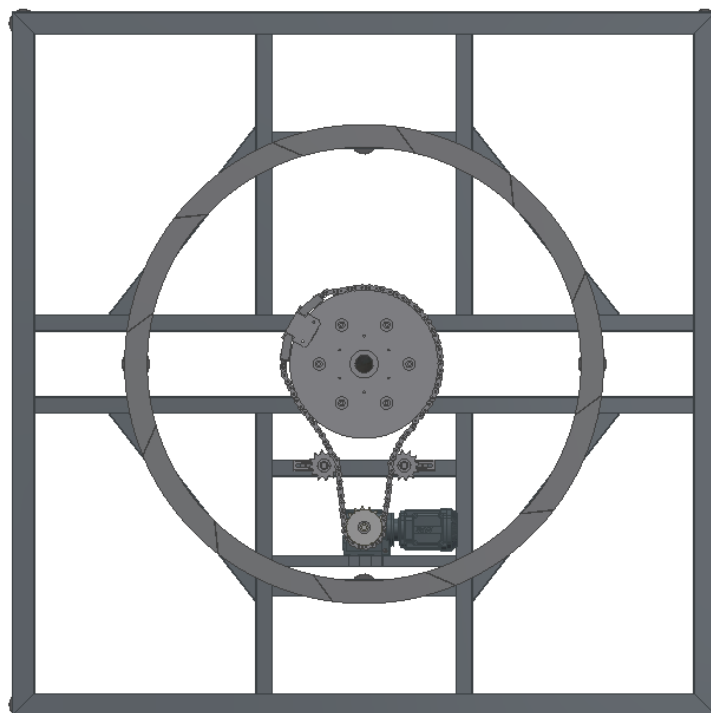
Zobrazení krytování válečkového stolu pomocí svařených plechů
